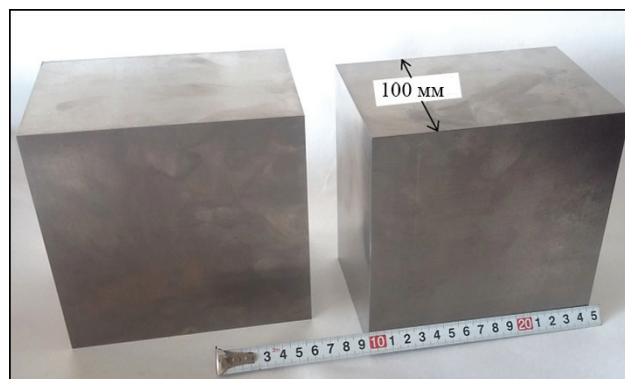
Зовнішній вигляд заготовок зі сплаву ВТ6
